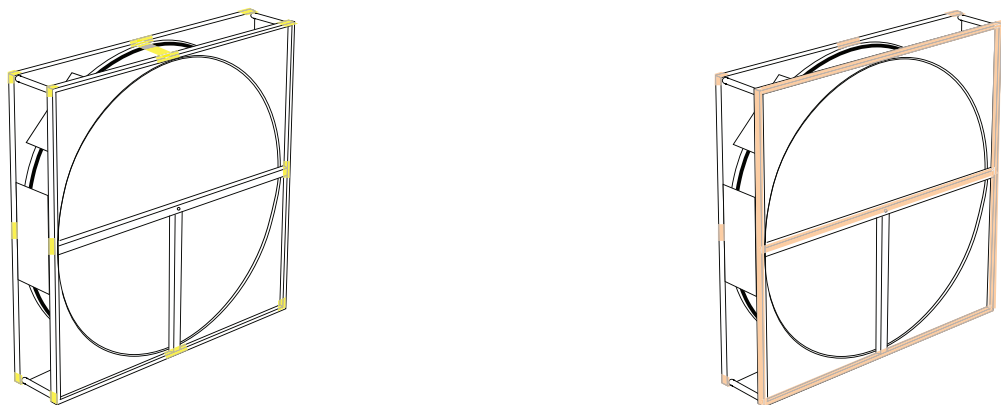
Stützpositionen, vertikaler Einbau (links) und horizontaler Einbau (rechts).
